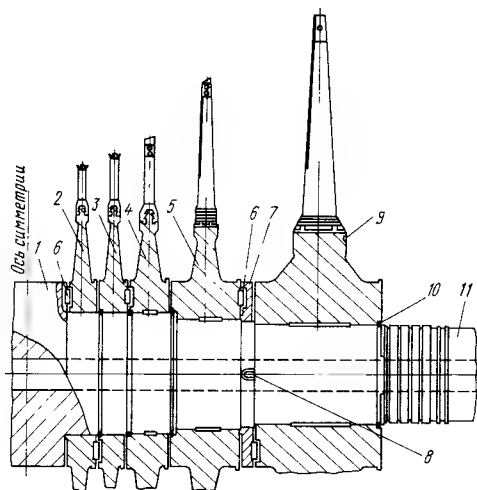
Сборный ротор двухпоточного ЦНД турбины ХТЗ:
